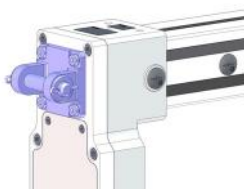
Bride pivotante (uniquement SLZ 63 P)
